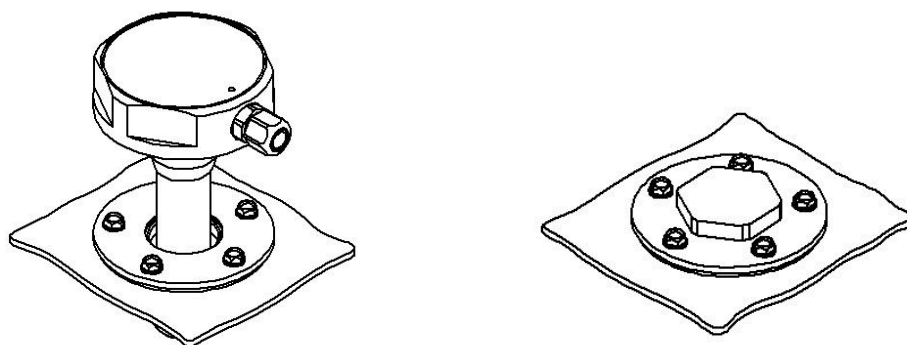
Полный демонтаж датчика уровня топлива и установка заглушки
